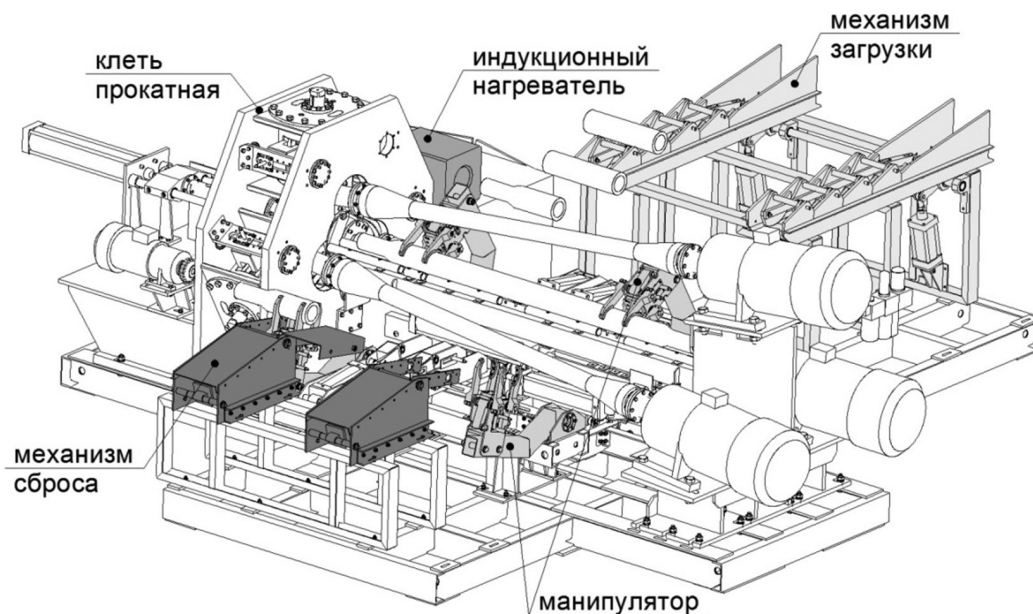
Автоматизированный комплекс поперечно-винтовой прокатки
